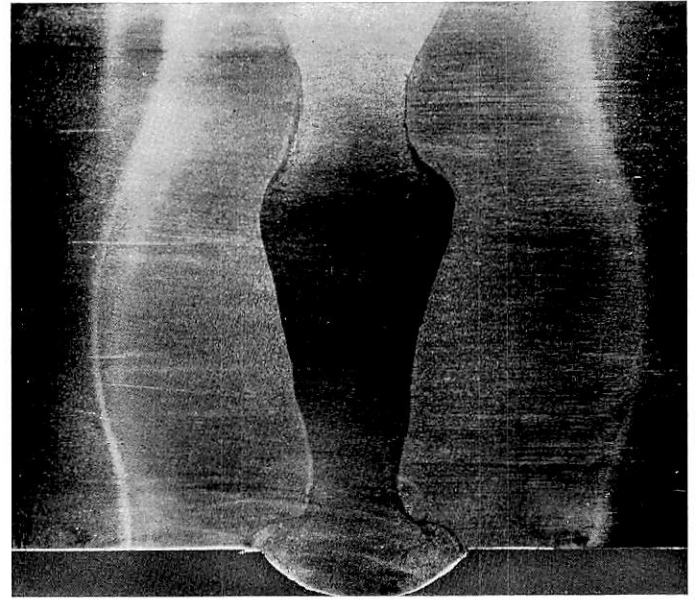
Zwischengußschweißung ohne Stauchung, geglüht.
